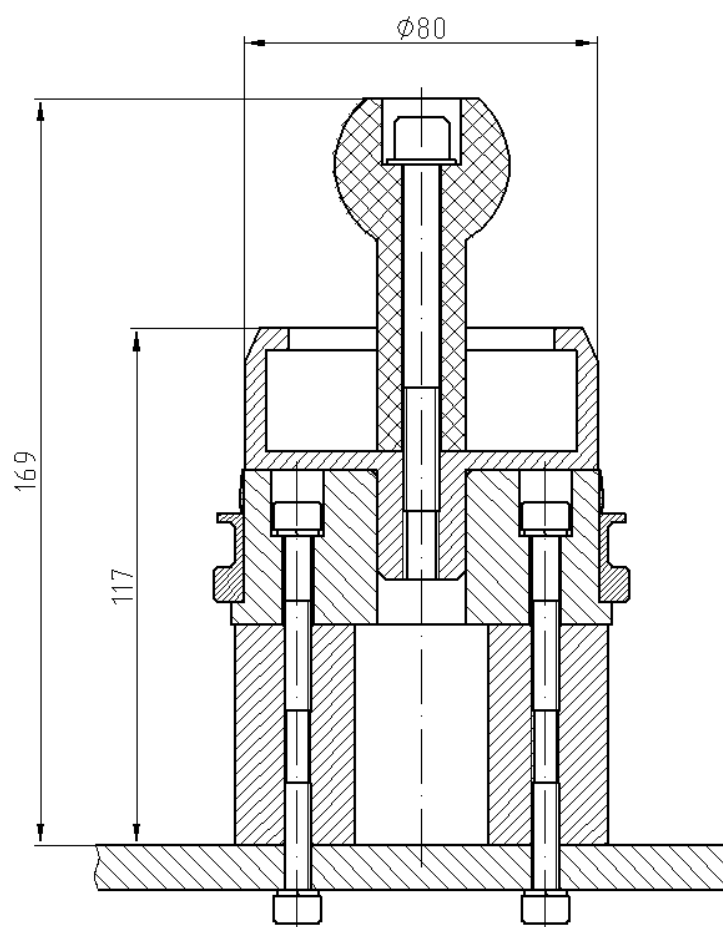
ЗМ 7820-4733, Приспособление для установки сальникодержателя с сальником без пружины
